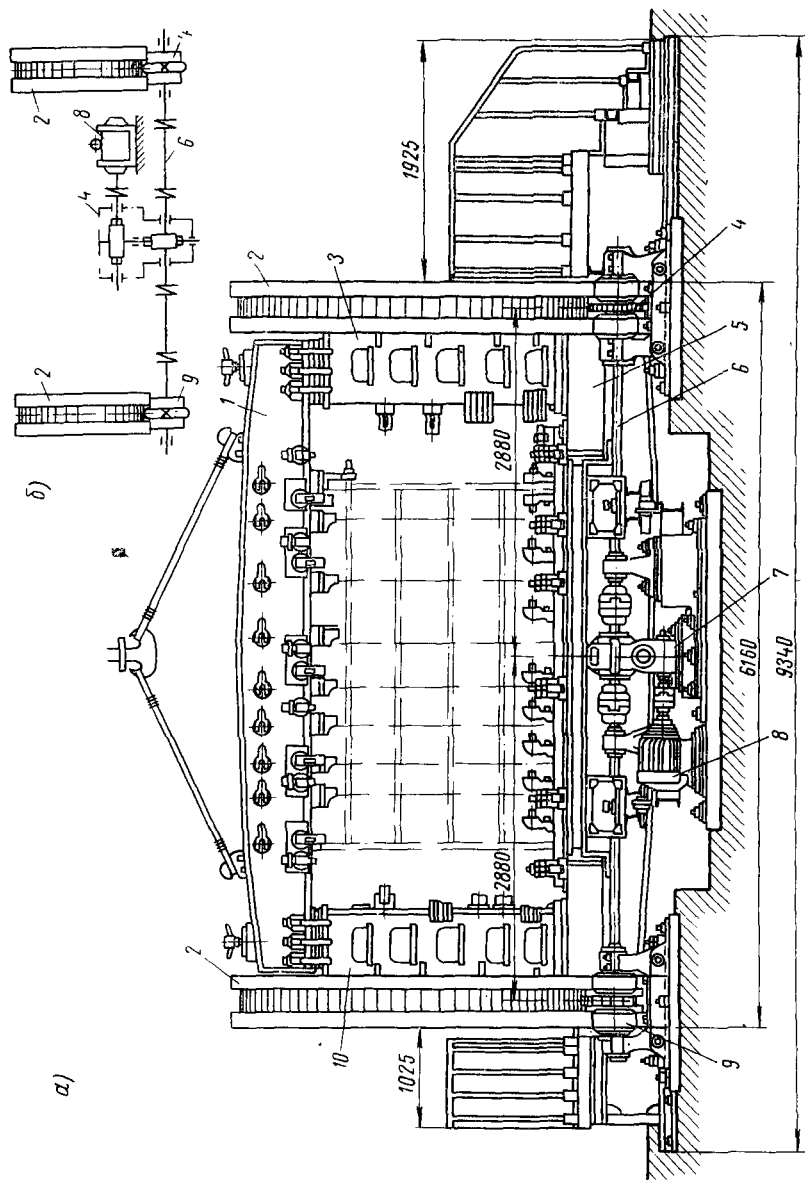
Стенд для сборки и сварки блока цилиндров тепловозного дизеля:
